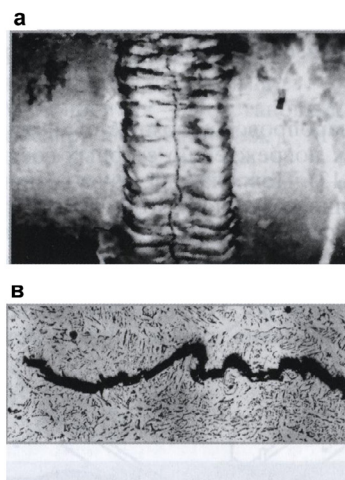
Примеры повреждения сварных соединений по наплавленному металлу:
